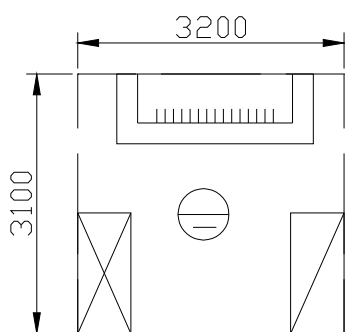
Схема организации рабочего места у ящичного шипорезного станка для резки
